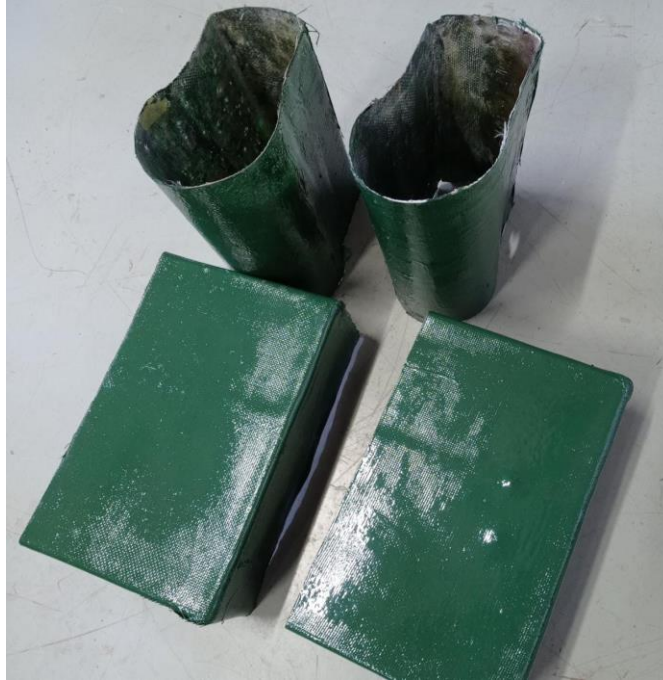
Molde perna (a) e molde caixa de baterias (b)
